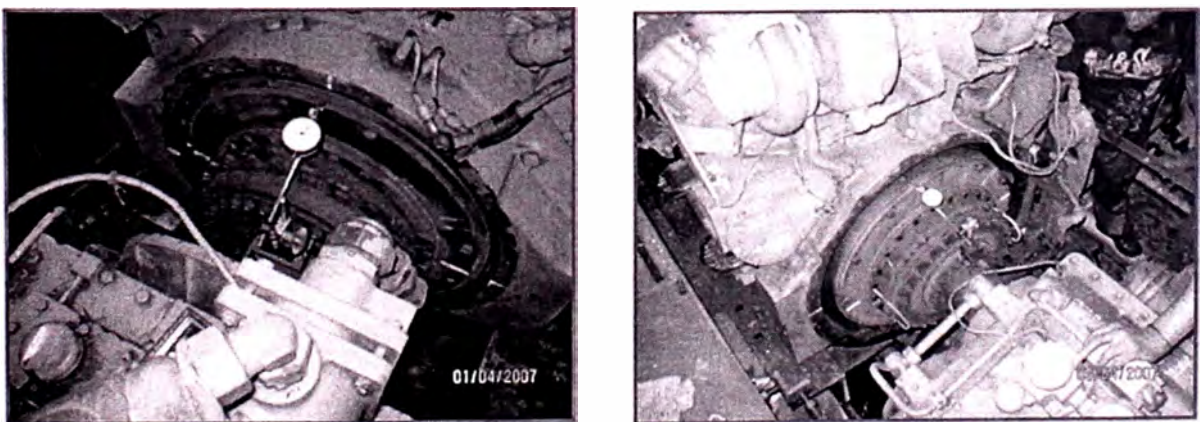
Vista del montaje del acoplamiento flexible entre el motor principal y la caja reductora.
